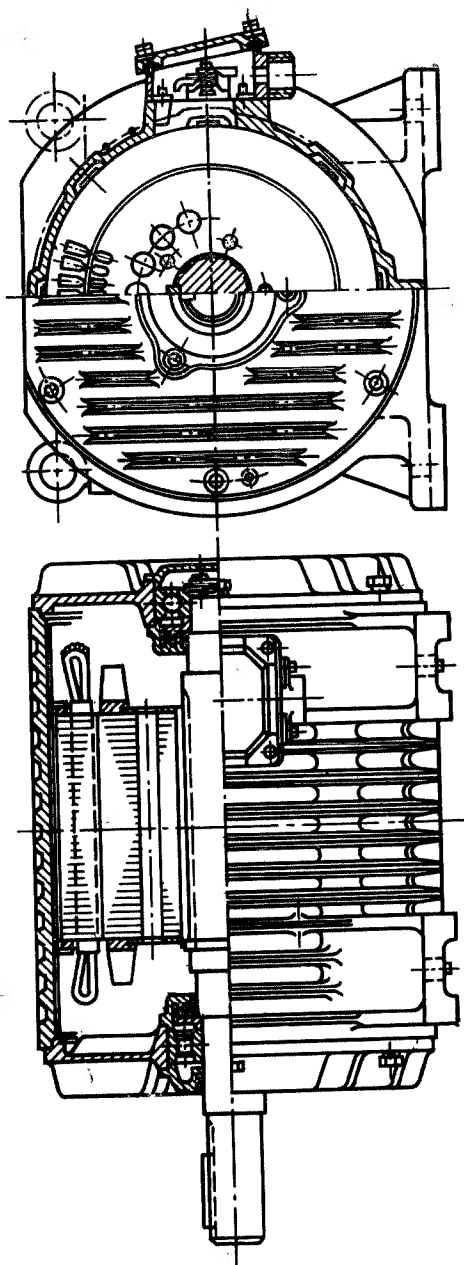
Общий вид рольгангового двигателя типа AP 6—8-го габаритов.
